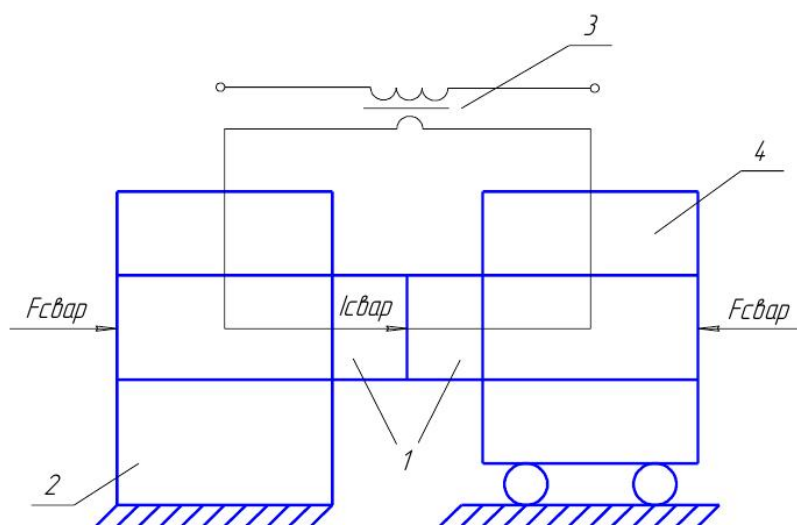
Схема стыковой контактной сварки
